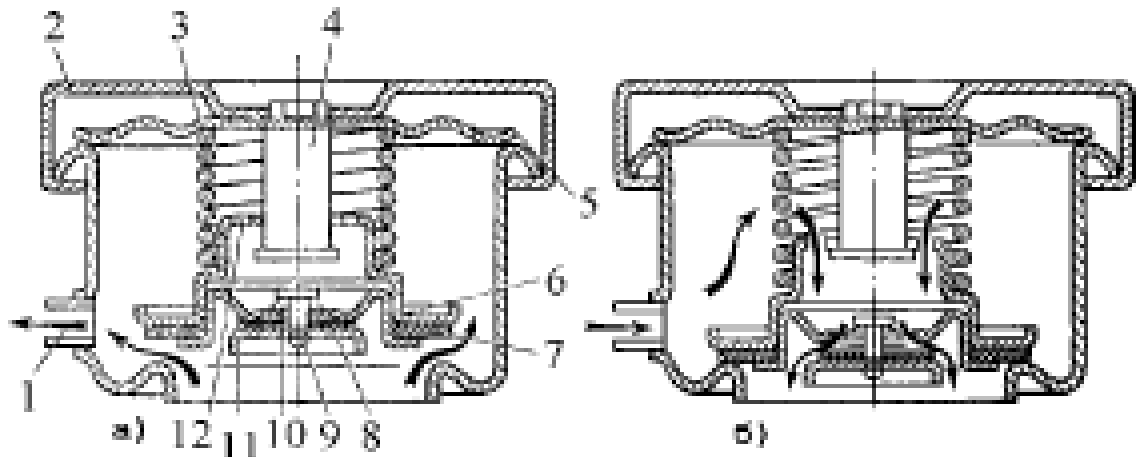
Паровоздушный клапан: а) выпуска пара; б) впуск воздуха: 1 – паропроводящая трубка; 2 – корпус пробки радиатора; 3 – пружина выпускного клапана; 4 – стойка; 5 – запирающая пружина; 6 – выпускной клапан; 7 – прокладка выпускного клапана; 8 – прокладка впускного клапана; 9 – впускной клапан; 10 – пружина впускного клапана; 11 – седло впускного клапана; 12 – отверстие для поступления воздуха
